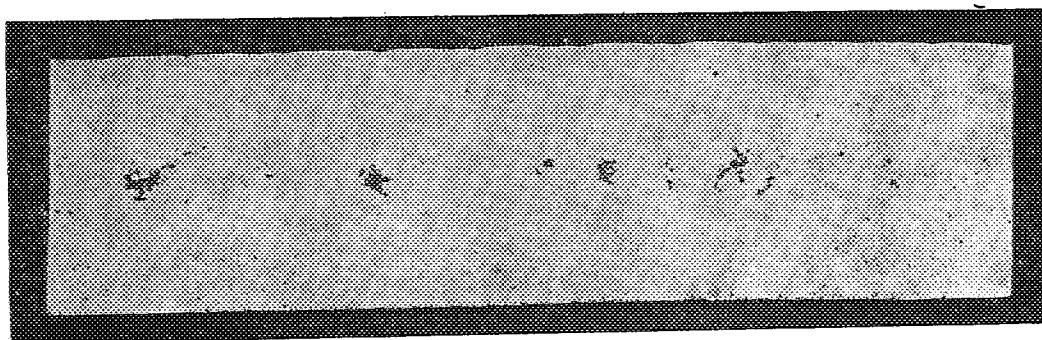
Section d'une barre d'acier montrant les défauts ouverts par le laminage.
